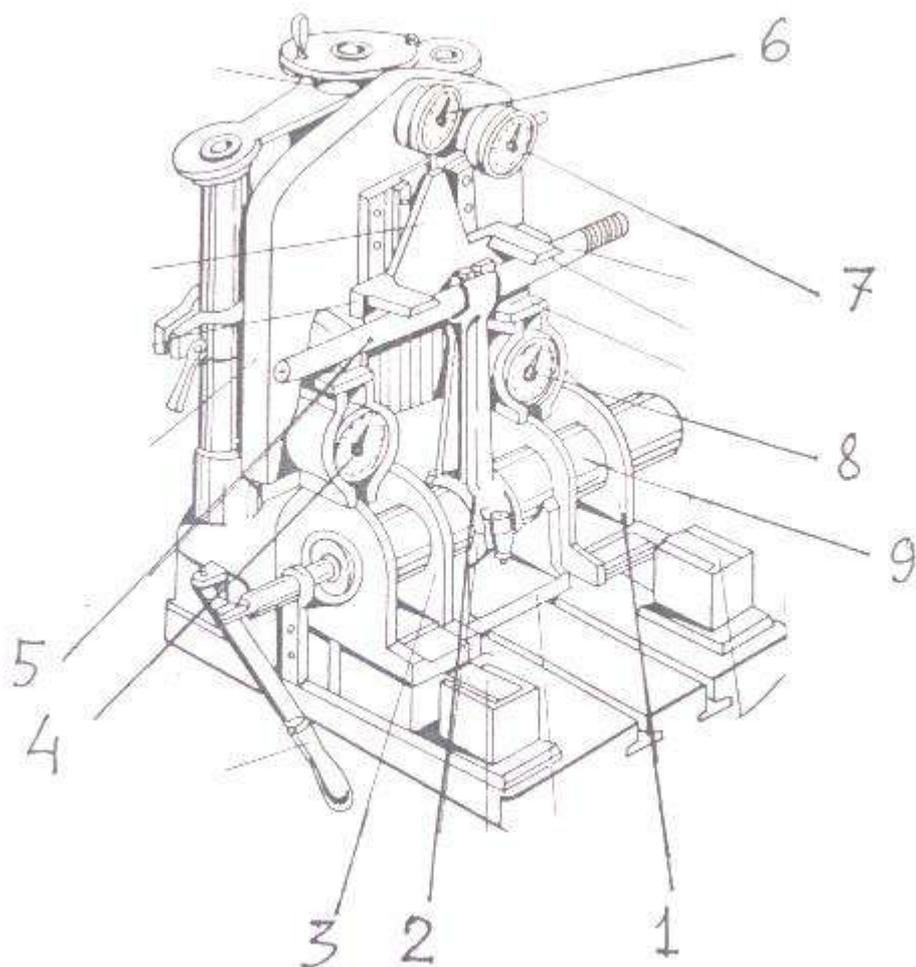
Приспособление для контроля и правки шатунов:
